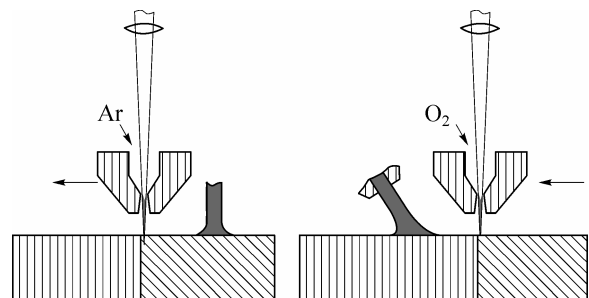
Применение нанопорошковых модификаторов при лазерной сварке.
